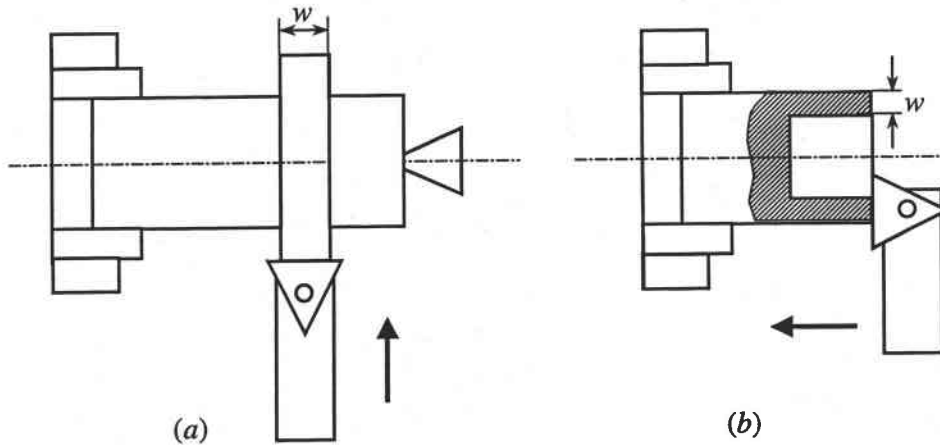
Exemples de coupe orthogonale. (a) Usinage d'un disque avec une avance radiale de l'outil. (b) Usinage d'un tube, l'avance de l'outil est axiale.
